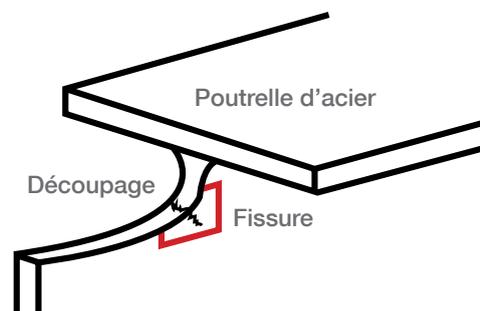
Fissure dans des poutrelles d'acier profilé après galvanisation
